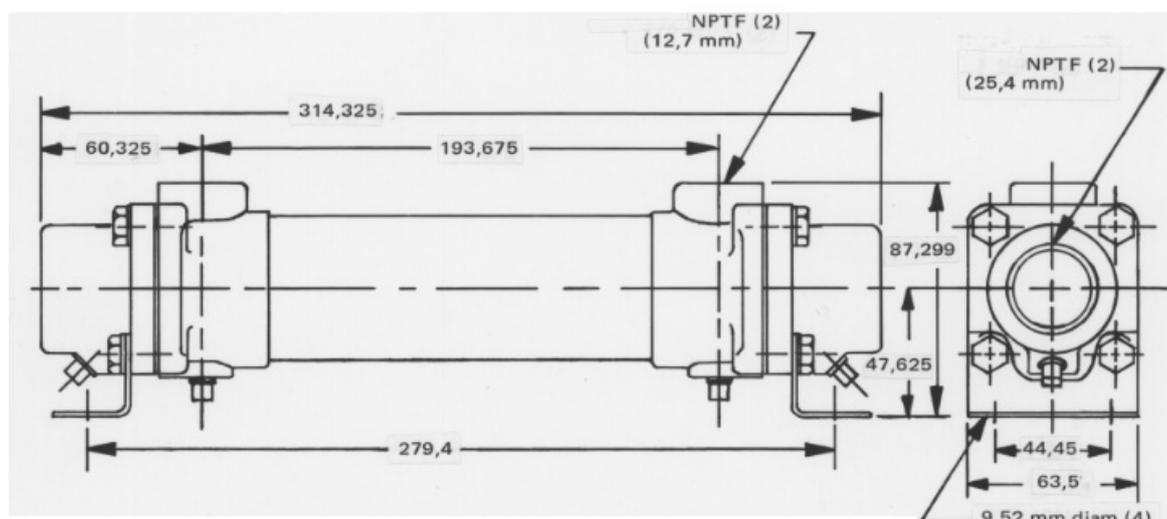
Dessin d'encombrement caractéristique d'un échangeur thermique séparé (ne pas utiliser pour le montage)
